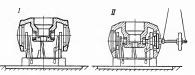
Схема сборки рычагов, серег и цапф без кантовки втулки.
